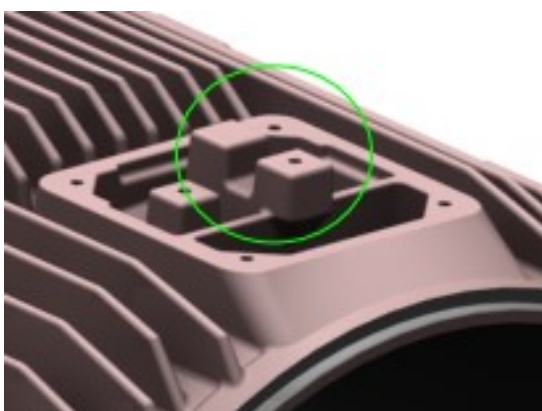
Kostra 5053818010102 po obrobení na obou strojích¹²
